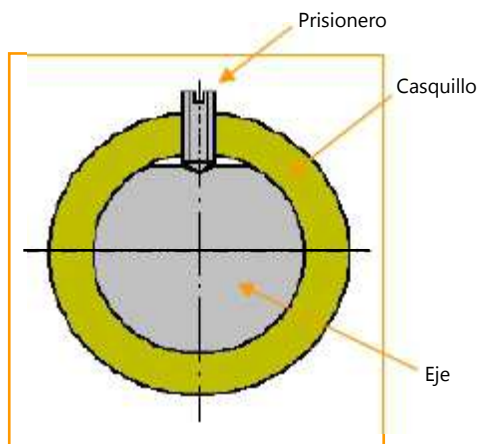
Unión de casquillo y eje mediante tornillo prisionero.
